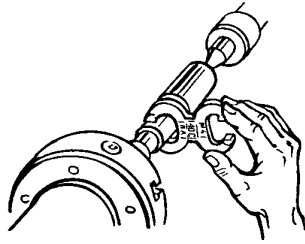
Контроль діаметра деталі калібром-скобою на токарному верстаті
